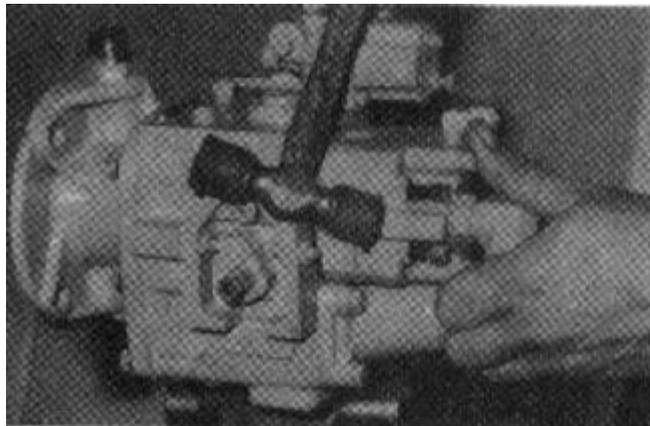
DESMONTAJE DE LA BOMBA DE ENGRANE
